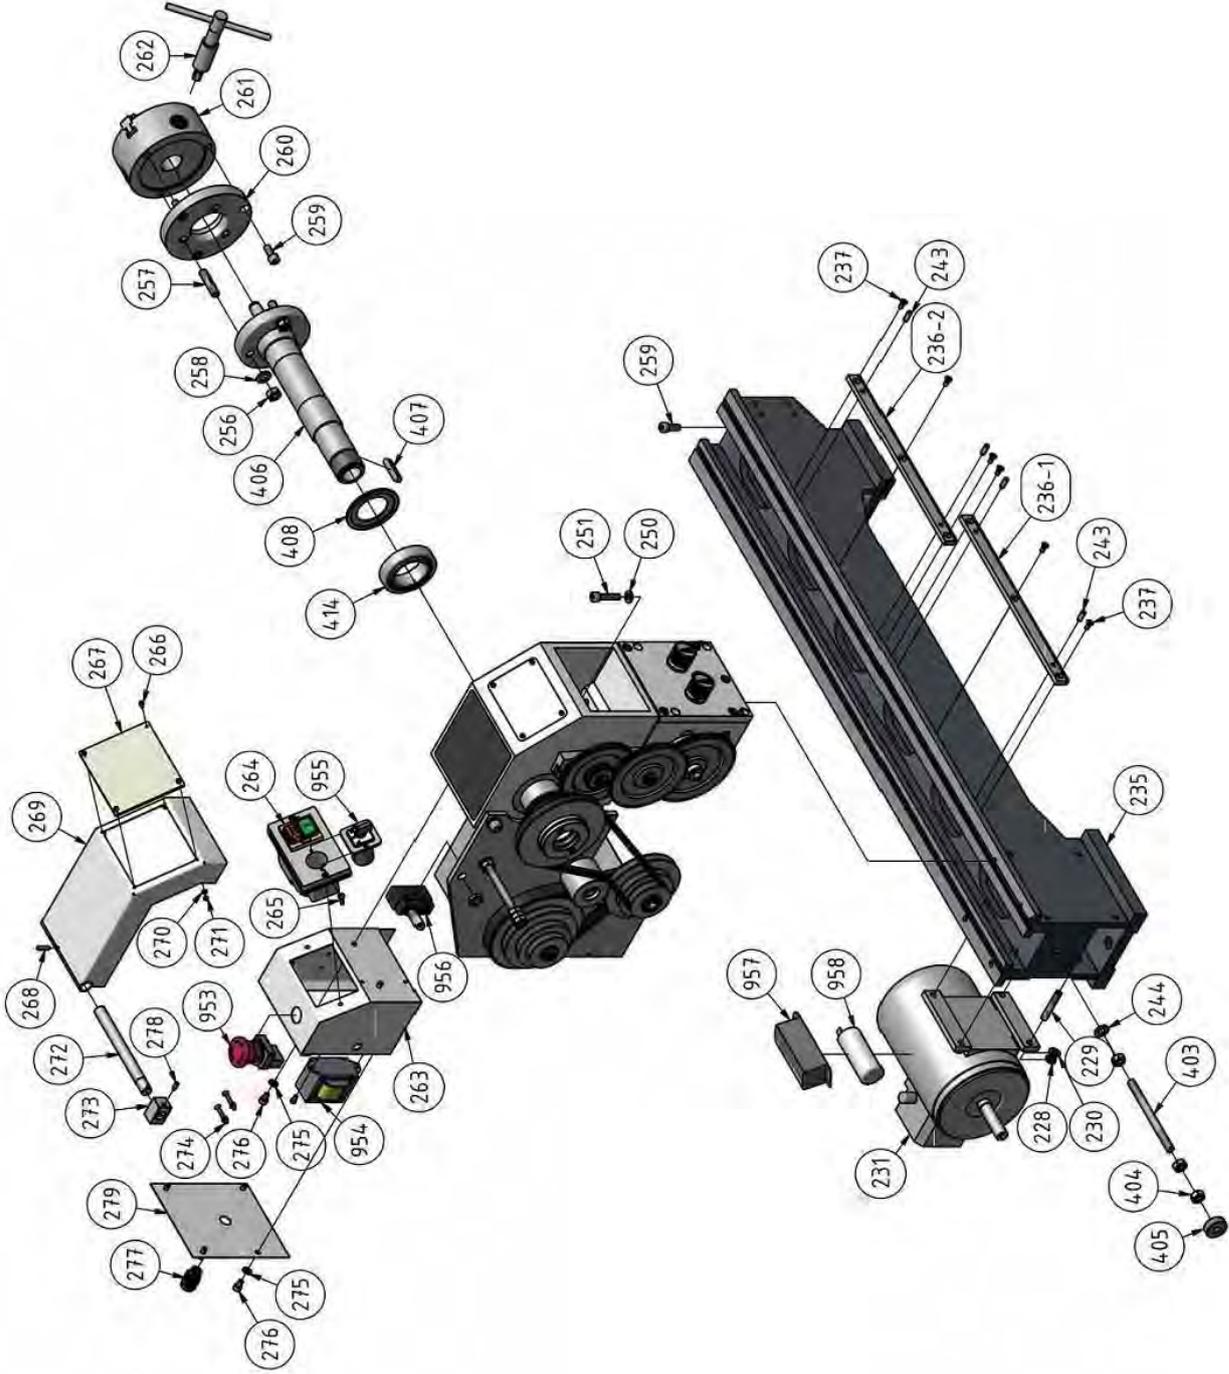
Spindelstock - Cabezal 2 de 2 - TU2506
